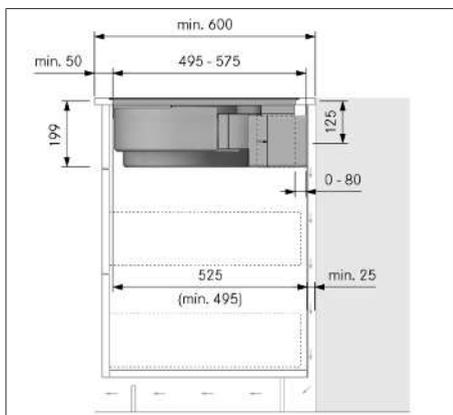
Dimensioni di montaggio con sistema filtrante, variante di montaggio A
